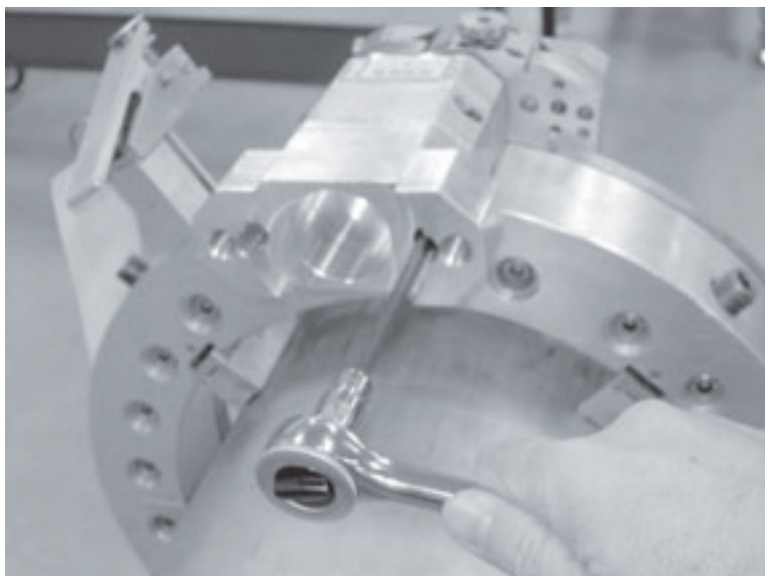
Затяните 2 шт. винтов, фиксирующих переходник гидравлического двигателя на корпусе ведущей шестерни.
